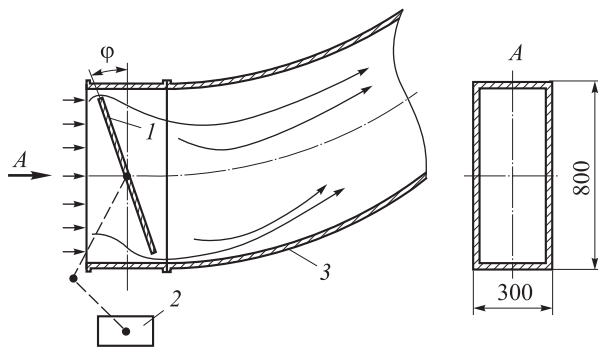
Схема всасывающего трубопровода ЦВН-500: 1 — плоская дроссельная заслонка; 2 — привод заслонки; 3 — трубопровод прямоугольного сечения
